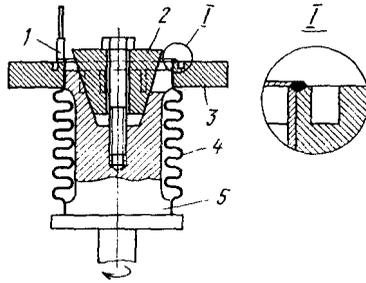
Сварка сиффона с фланцем:
